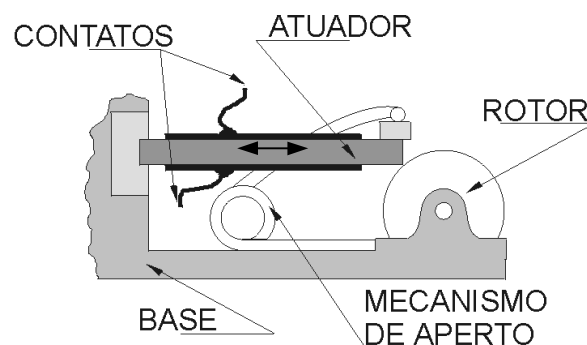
Esquema de construção de um motor piezelétrico de rotação com estator ativo e rotor passivo (Lavrinenko et al, 1998).
